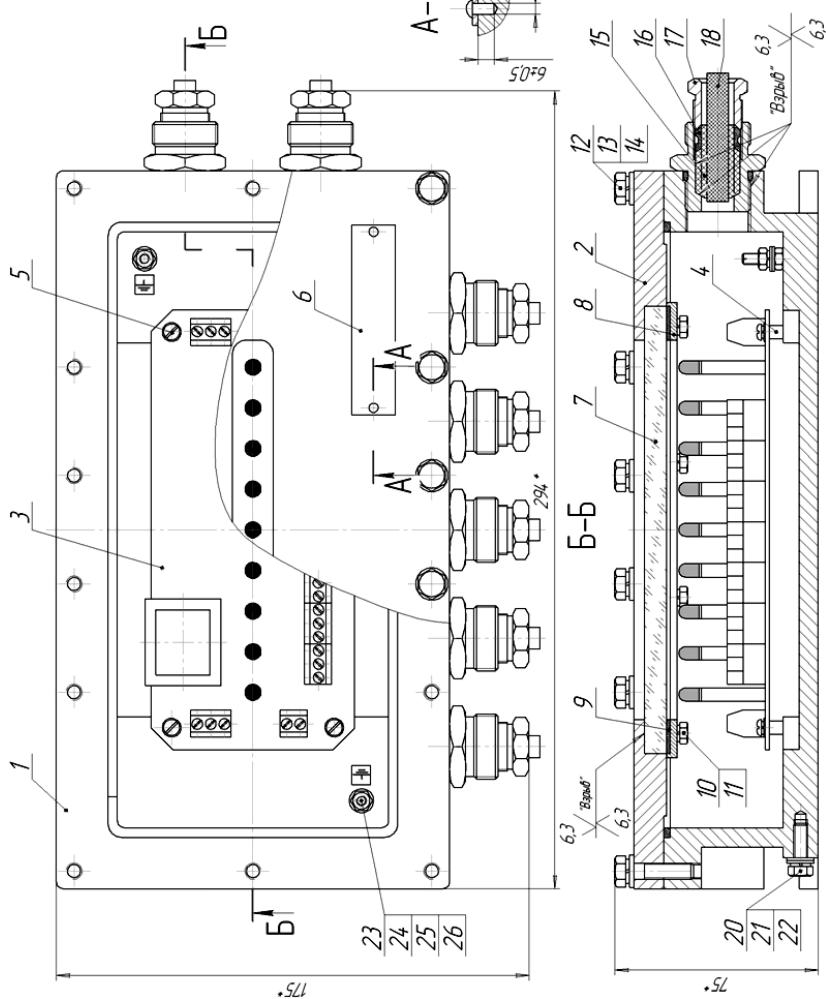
БК обычного исполнения. Внешний вид, габаритные и установочные размеры
